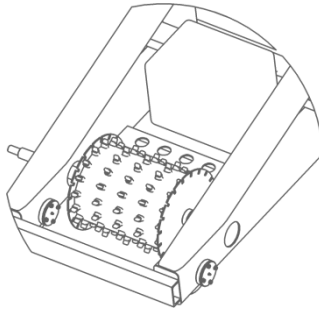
Общее устройство быстросъемное фрезерное оборудования: 1 - колесо (4 шт); 2 - фреза; 3 - диск Ф380; 4 - рама; 5 - бункер для термопластика; 6 - крепление воздуховода; 7 - вал фрезы.
